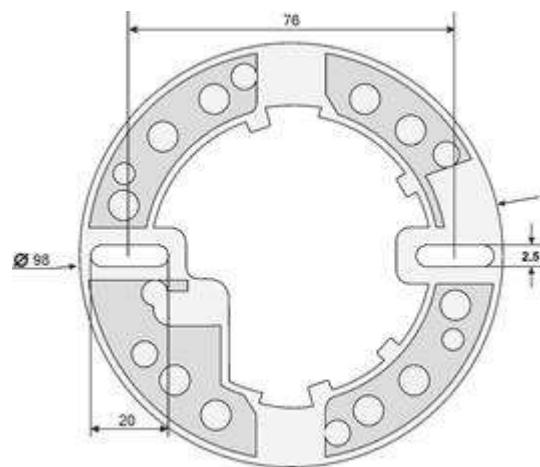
Установочный чертеж Р485 и RS485/FTTx-S-SC
